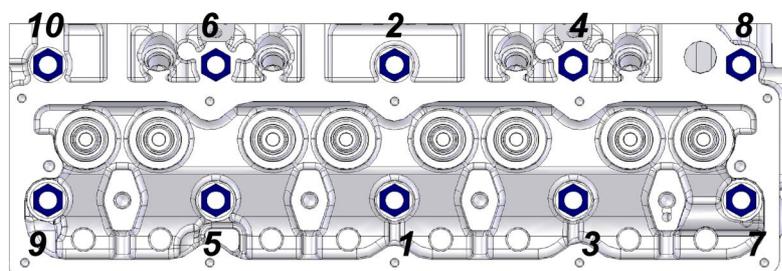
Порядок подтяжки гаек головки блока цилиндров
